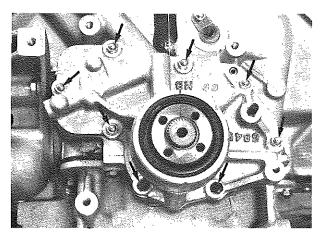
Dadi e viti di fissaggio Nuts and fixing screws
